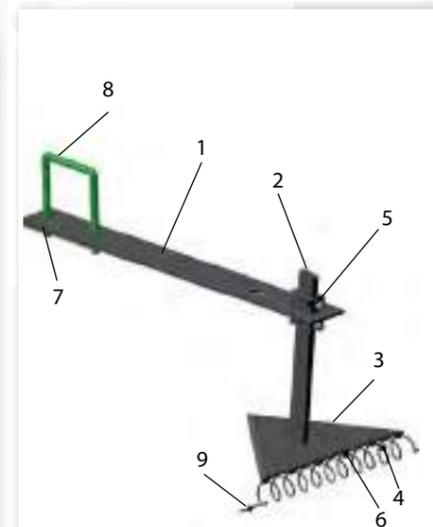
Объемная модель секции инновационного пропашного культиватора: 1 — грядиль, 2 — стойка, 3 — треугольный лемех, 4 — спираль, 5 — держатели, 6 — зацеп, 7 — упорная пластина, 8 — скоба, 9 — пружинный палец
